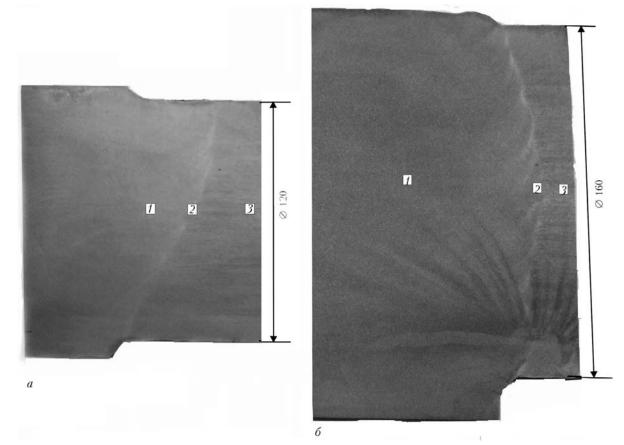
Макрошлифы зоны соединения патрубка с литым корпусом задвижки Ду50 (a) и Ду80 (b): t- литой электрошлаковый металл; 2- линия сплавления; 3- зона термического влияния на металле патрубка
